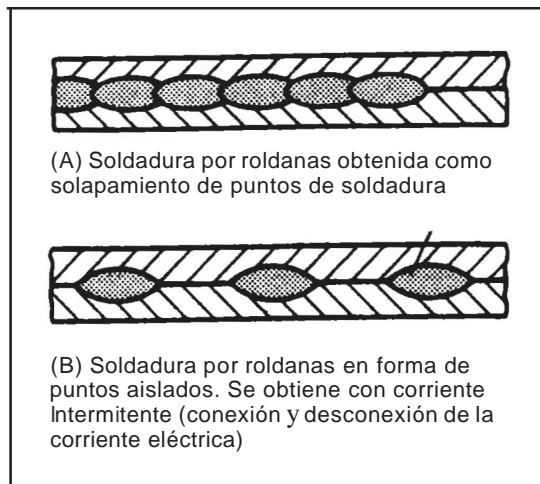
SOLDADURAS POR ROLDANAS
